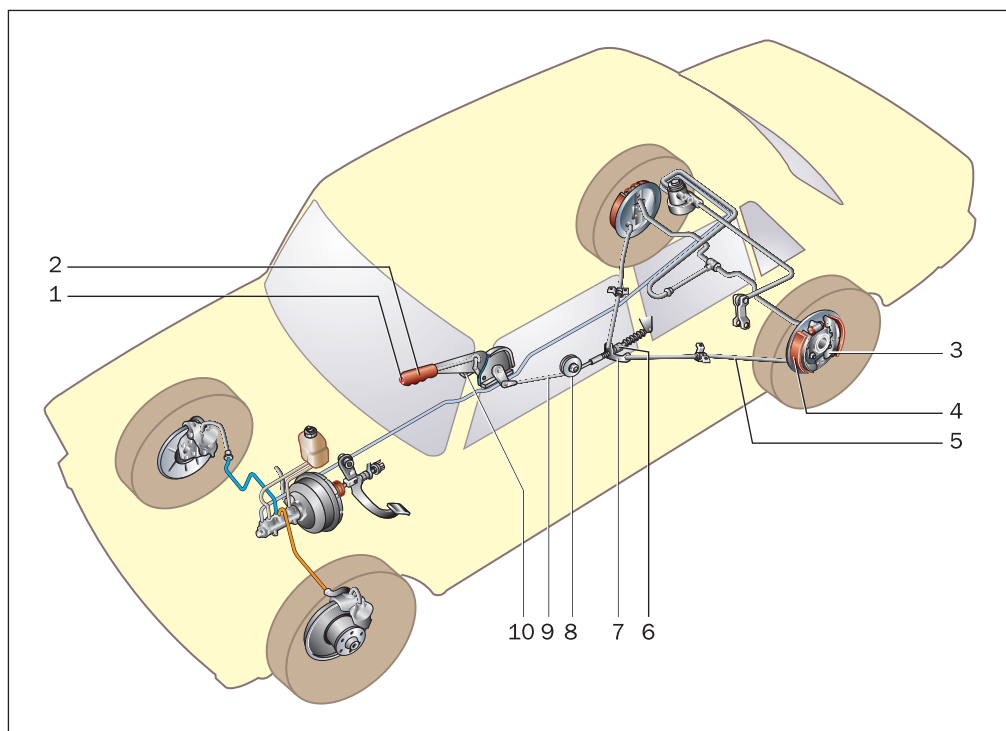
Механический привод стояночной тормозной системы: 1 — кнопка рычага привода стояночного тормоза; 2 — рычаг привода стояночного тормоза; 3 — рычаг ручного привода колодок; 4 — задние тормозные колодки; 5 — задний трос; 6 — регулировочная гайка с контргайкой; 7 — уравниватель заднего троса; 8 — направляющий ролик; 9 — передний трос; 10 — упор выключателя сигнализатора включения стояночного тормоза
